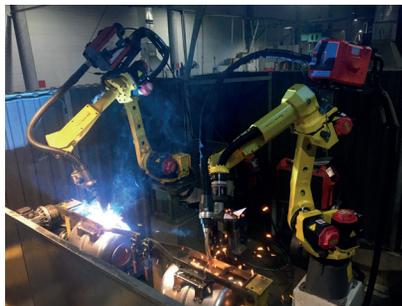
Робототехнологический комплекс РК754-2 для МИГ-сварки малогабаритных изделий одновременно двумя роботами
